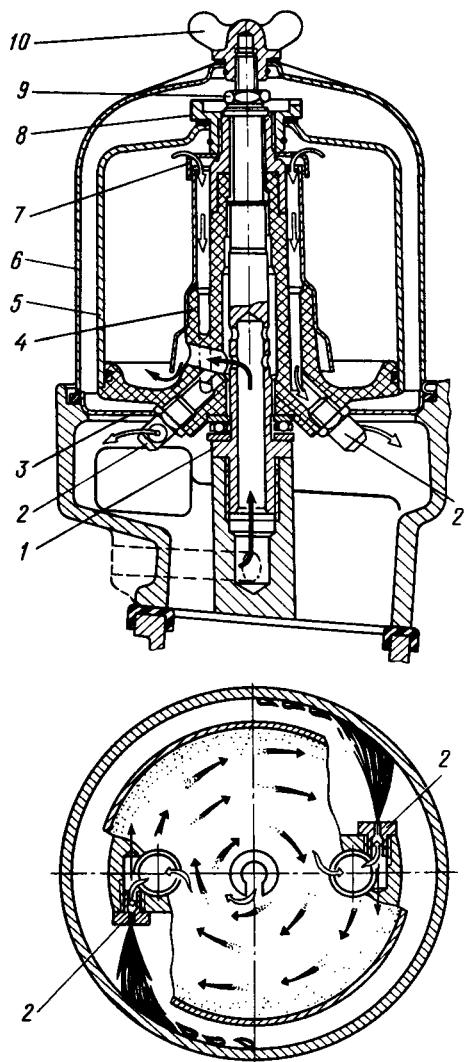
Фильтр центробежной очистки масла двигателя ЗМЗ-53:
